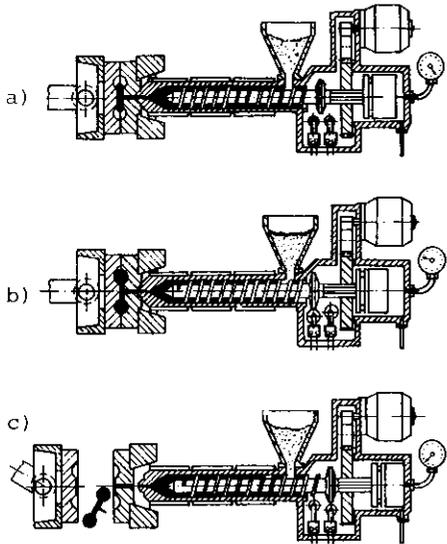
Seqüência do processo de moldagem por injeção em máquina de parafuso. a) O parafuso é impelido por um pistão hidráulico e comprime, como um êmbolo, a massa plástica contida no molde; b) O molde está carregado e a massa se solidifica dentro do molde; c) O parafuso introduz o material plastificado no espaço à frente de sua cabeça, ao mesmo tempo em que se desmolda o objeto recém injetado.
